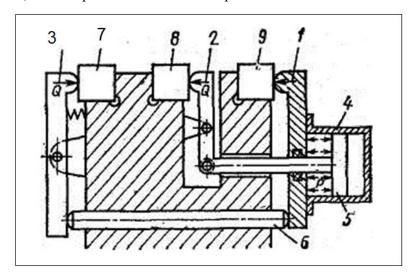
Схема многоместного приспособления с плавающим цилиндром
